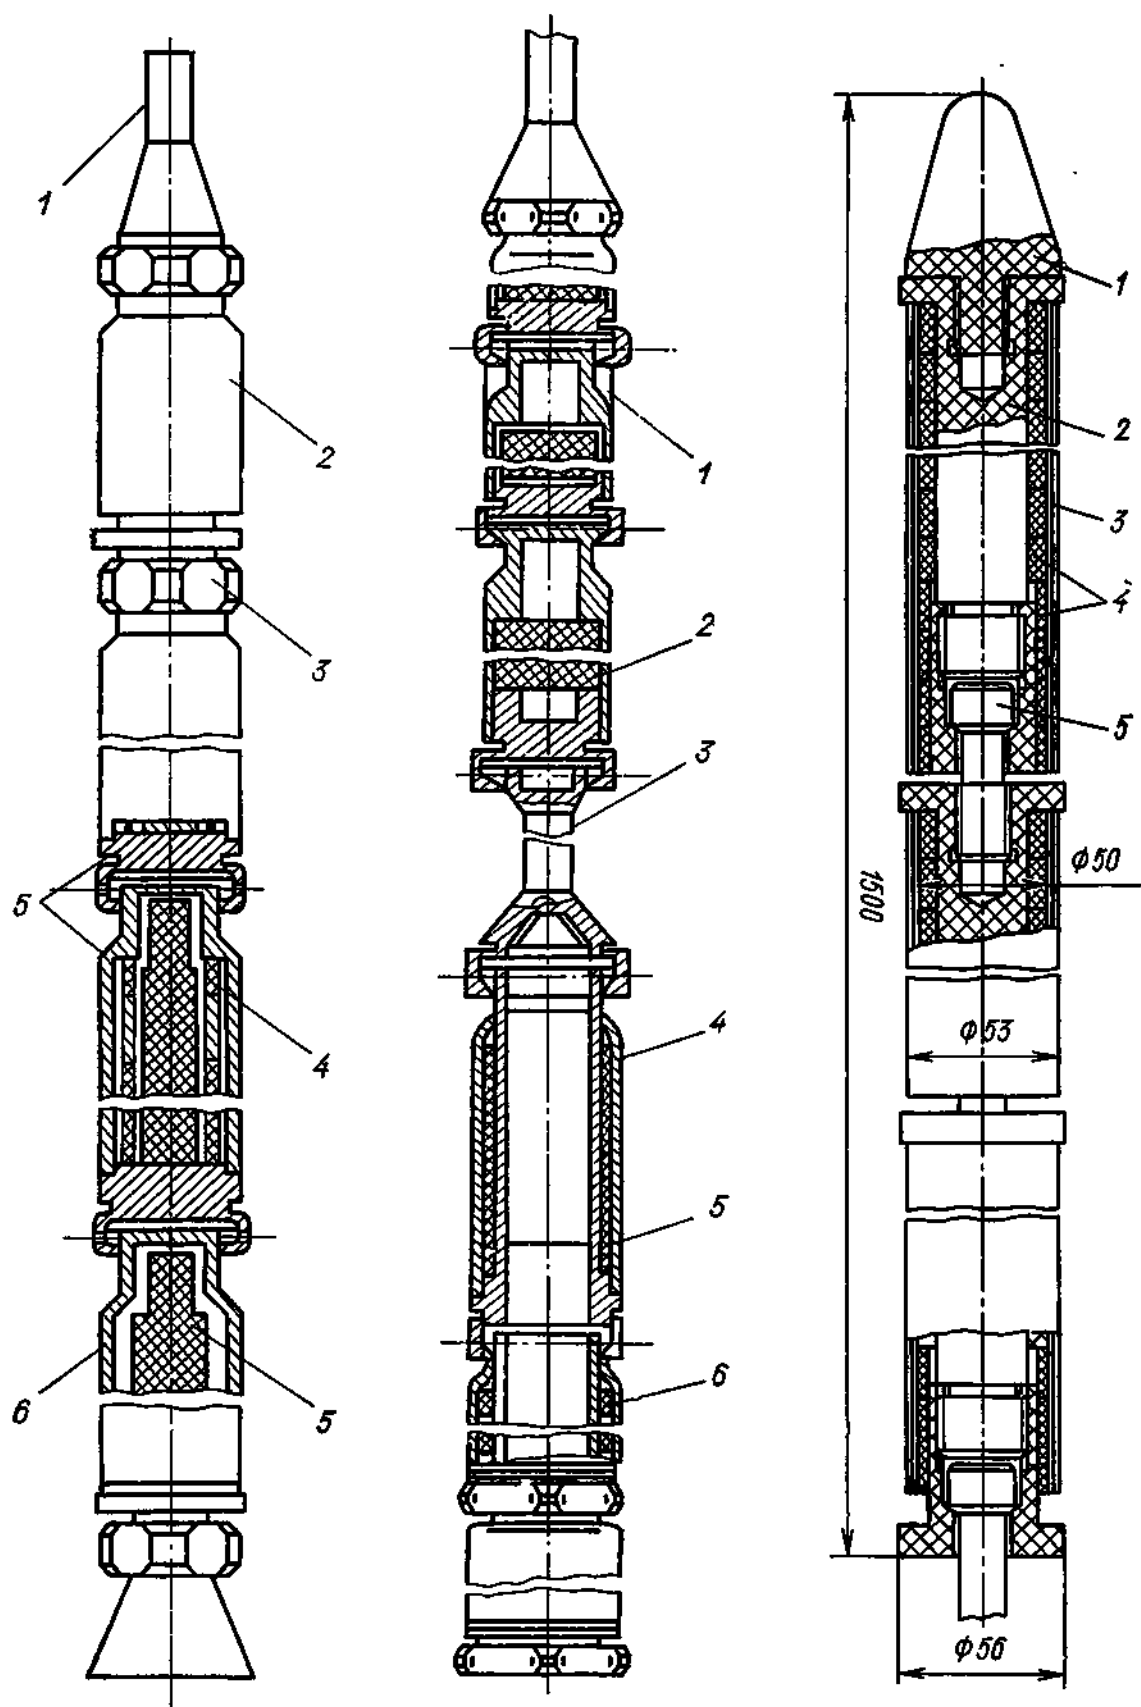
Конструкция стержня РР реактора РБМК-1000:
